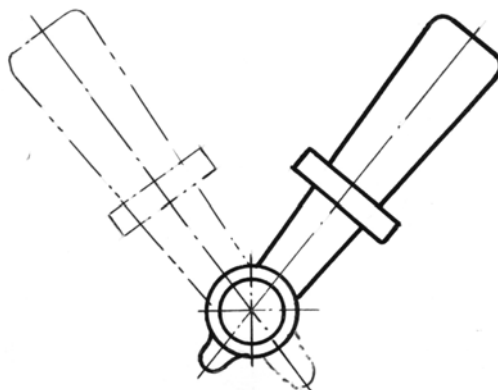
Изображение подвижных деталей на сборочном чертеже
